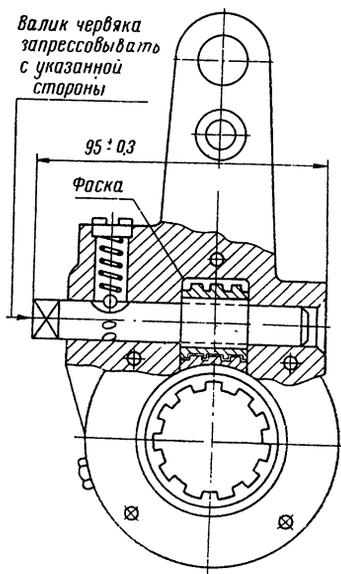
Запрессовка валика регулировочного механизма колесных тормозов
